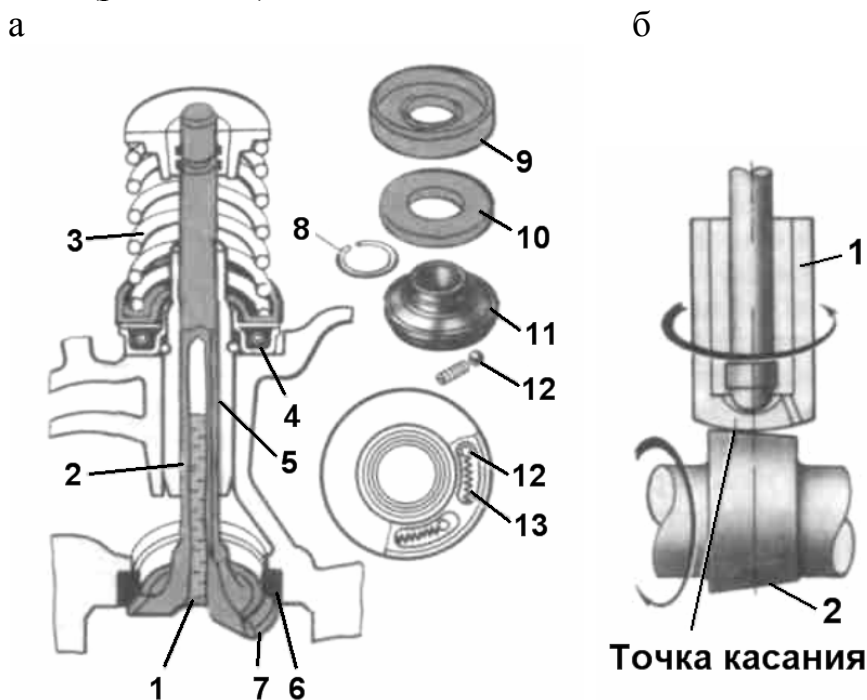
Механизмы, обеспечивающие равномерный износ деталей:
